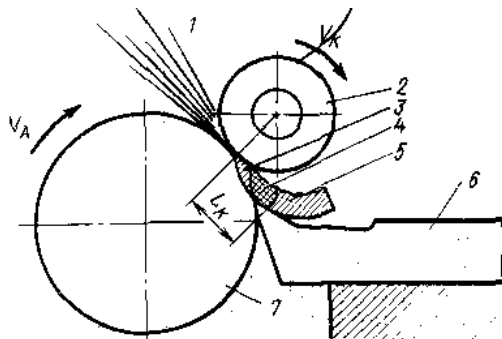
Схема абразивно-лезвийного способа обработки [1]:
